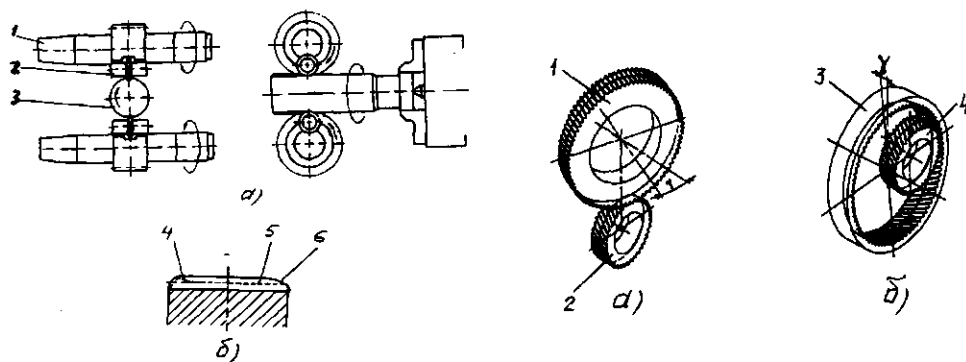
Зубохонингование цилиндрических колес: а – хонем с внешним зацеплением; б – хонем с внутренним зацеплением
